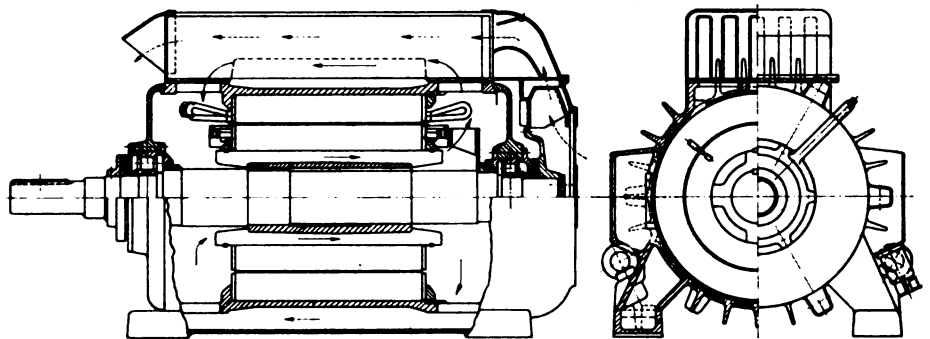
Mantelgekühlter Motor mit Oberflächenkühlung.
